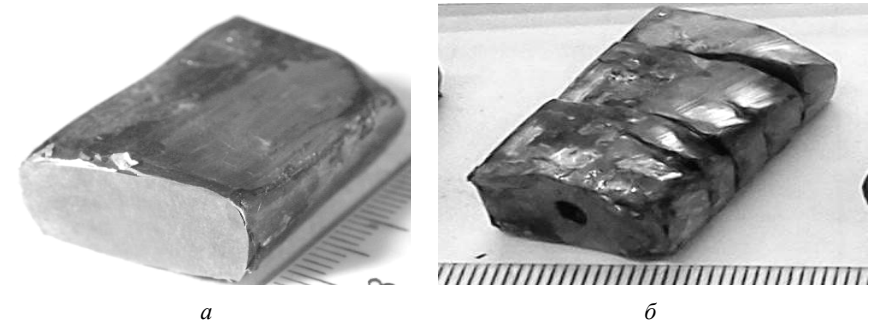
Вид заготовок после винтовой экструзии титана BT1-0 в различном исходном состоянии: а – исходная заготовка – пруток; б – исходная заготовка – слиток ВДП
